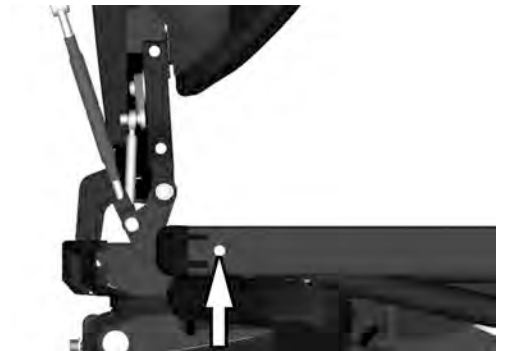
Hintere Befestigungsschraube der UniTrack-Schiene.
